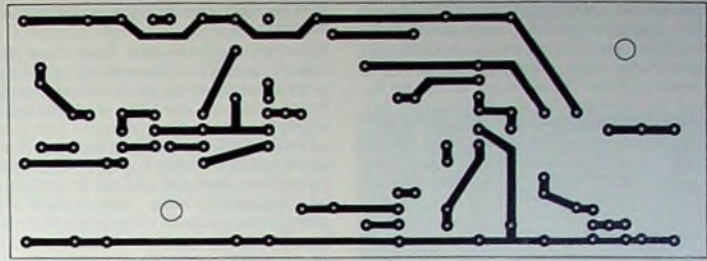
Printplatte I für die Schaltung nach Bild 4 im Maßstab 1:1
